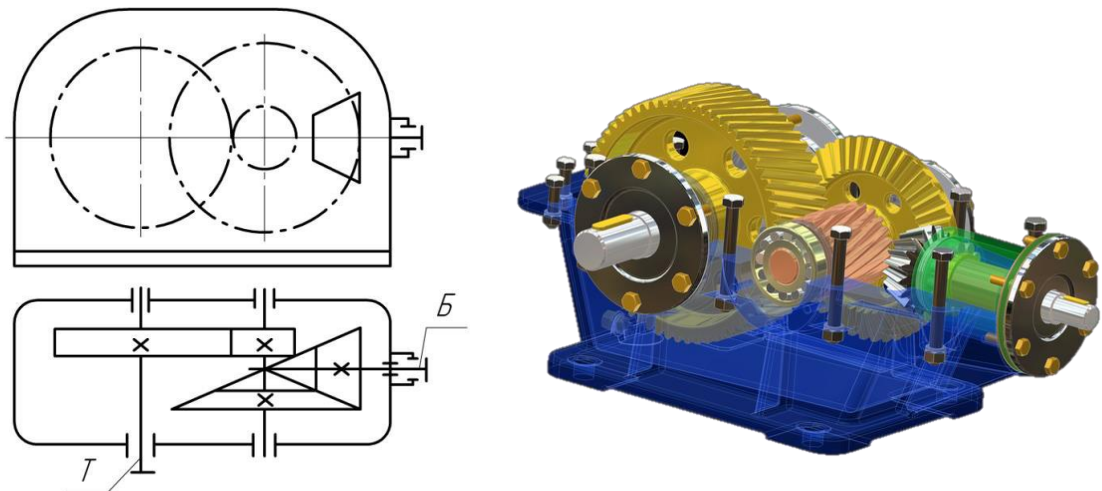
Двухступенчатый горизонтальный коническо-цилиндрический редуктор
